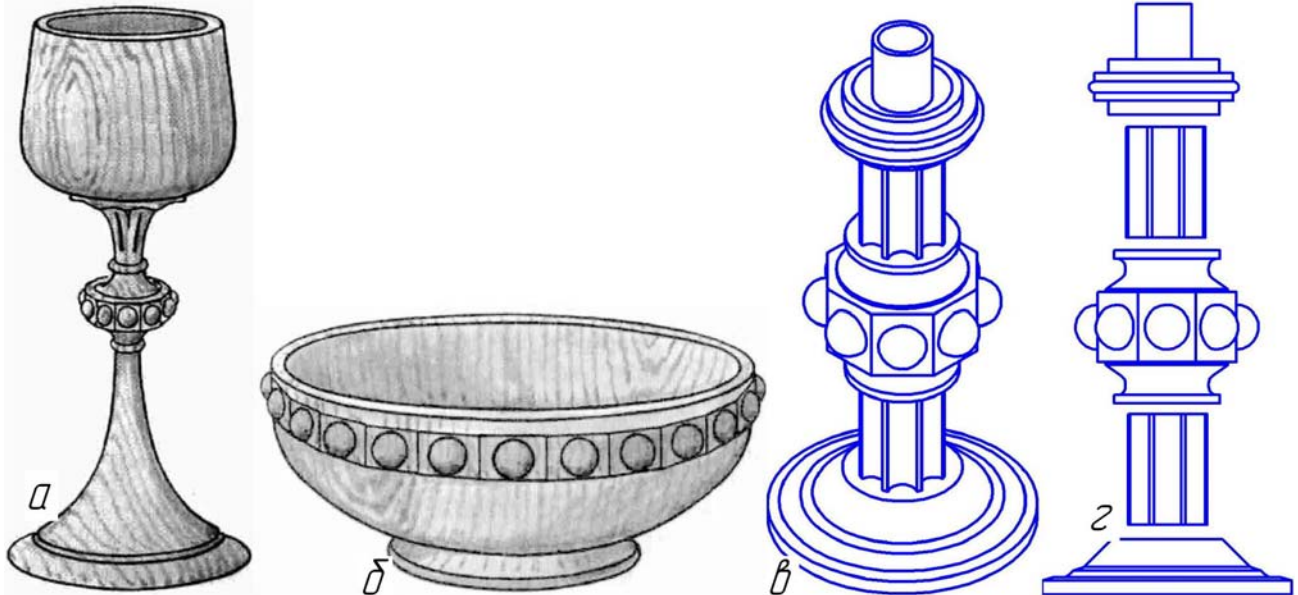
Варіанти монтажу деталей з декількома осями фрезерування:
